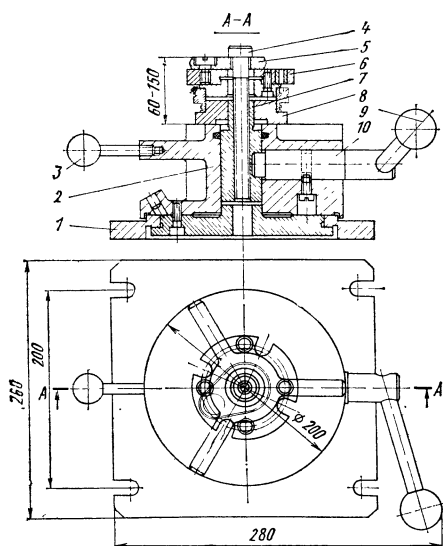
Компонка специализированного переналаживаемого кондуктора для сверления отверстий в деталях типа втулок и фланцев
